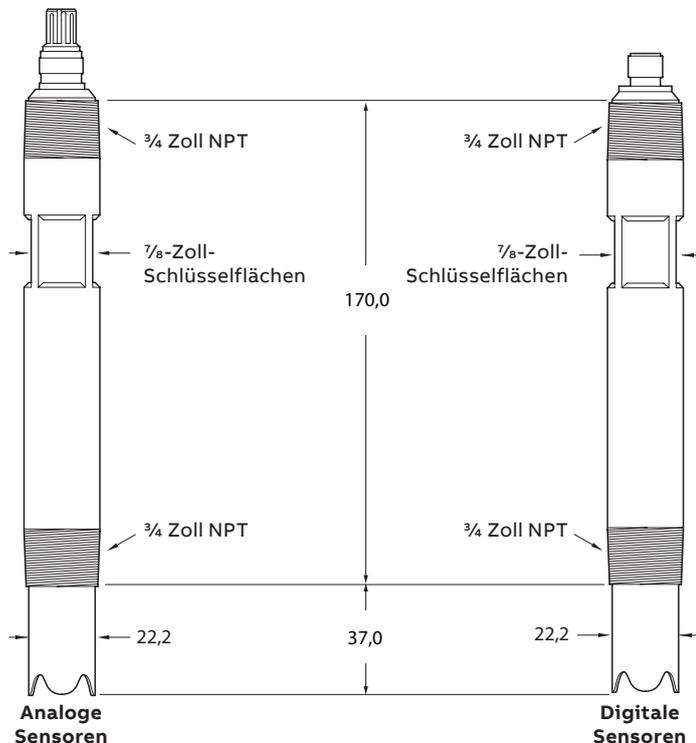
Abmessungen gekerbtes Sensorgehäuse
